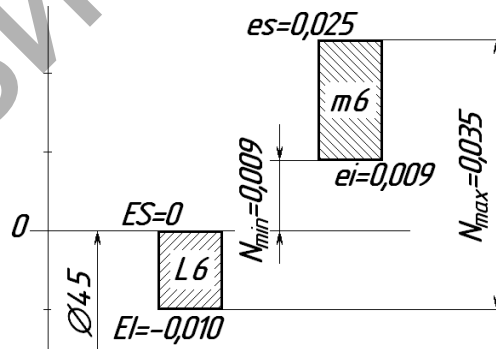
Схема расположения полей допусков посадки внутреннего кольца шарикоподшипника радиального 6—309 на вал
